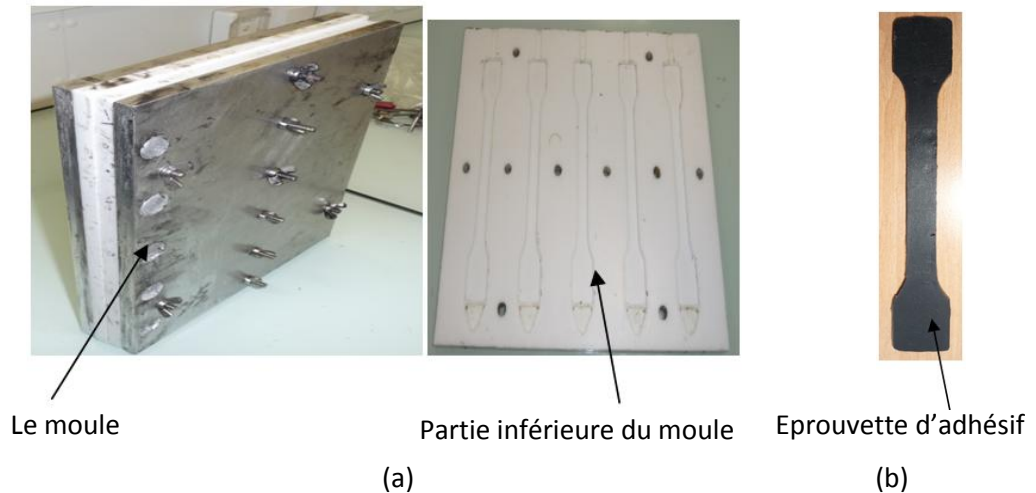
Présentation du moule pour la fabrication des éprouvettes.
